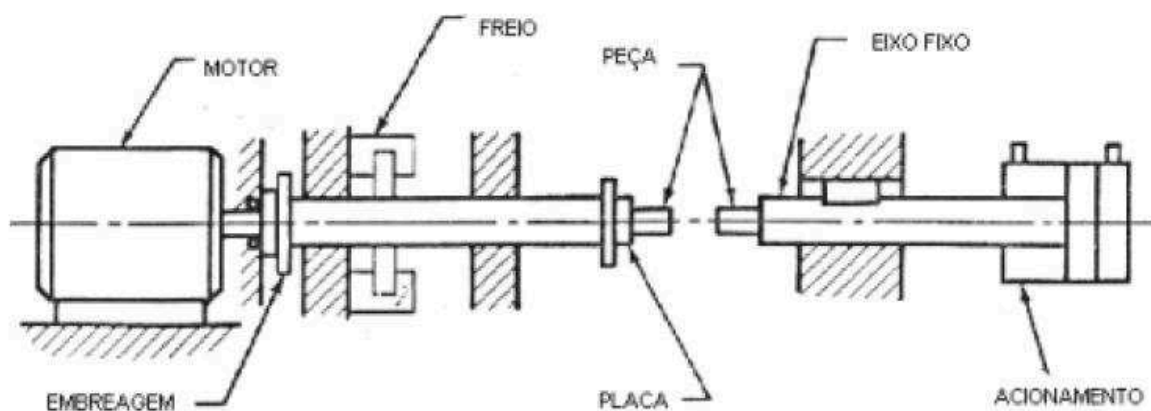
Equipamento de soldagem por fricção – SILVA (2011)
